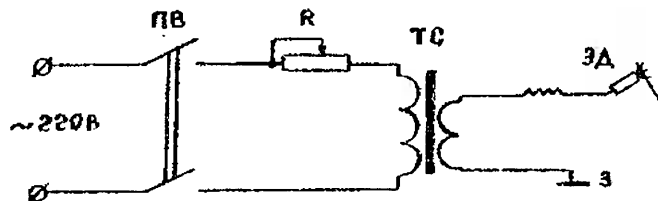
Схема подключения трансформатора к сети: ПВ - пакетный выключатель; ТС - трансформатор сварочный; R - реостат; ЭД - электродержатель; 3 - корпус свариваемой детали.
